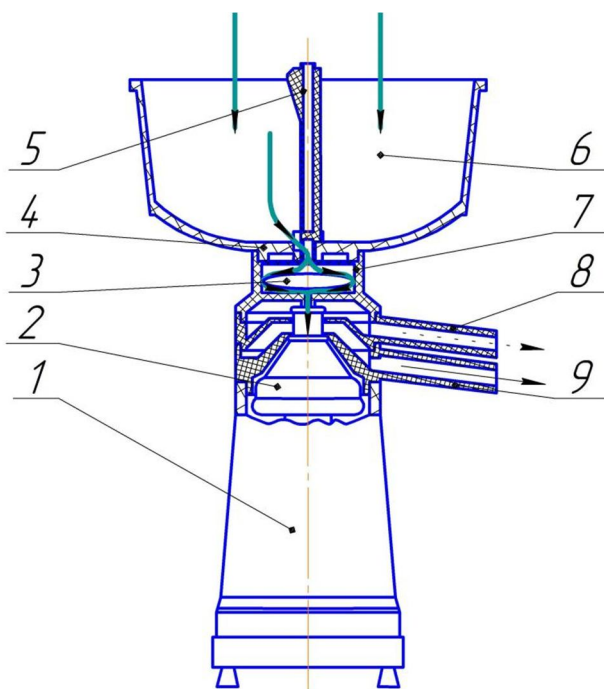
Конструктивная схема сепаратора-сливкоотделителя по патенту РФ на изобретение № 2539759: 1 – корпус; 2 – барабан, 3 – поплавок; 4 – приемно-выводное устройство; 5 – кран; 6 – молокоприемник, 7 – поплавковая камера; 8 – патрубок сливок; 9 – патрубок обезжиренного молока
